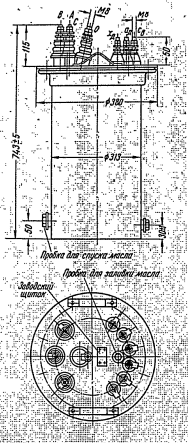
Габаритные размеры трансформатора напряжения типа НТМИ-6
